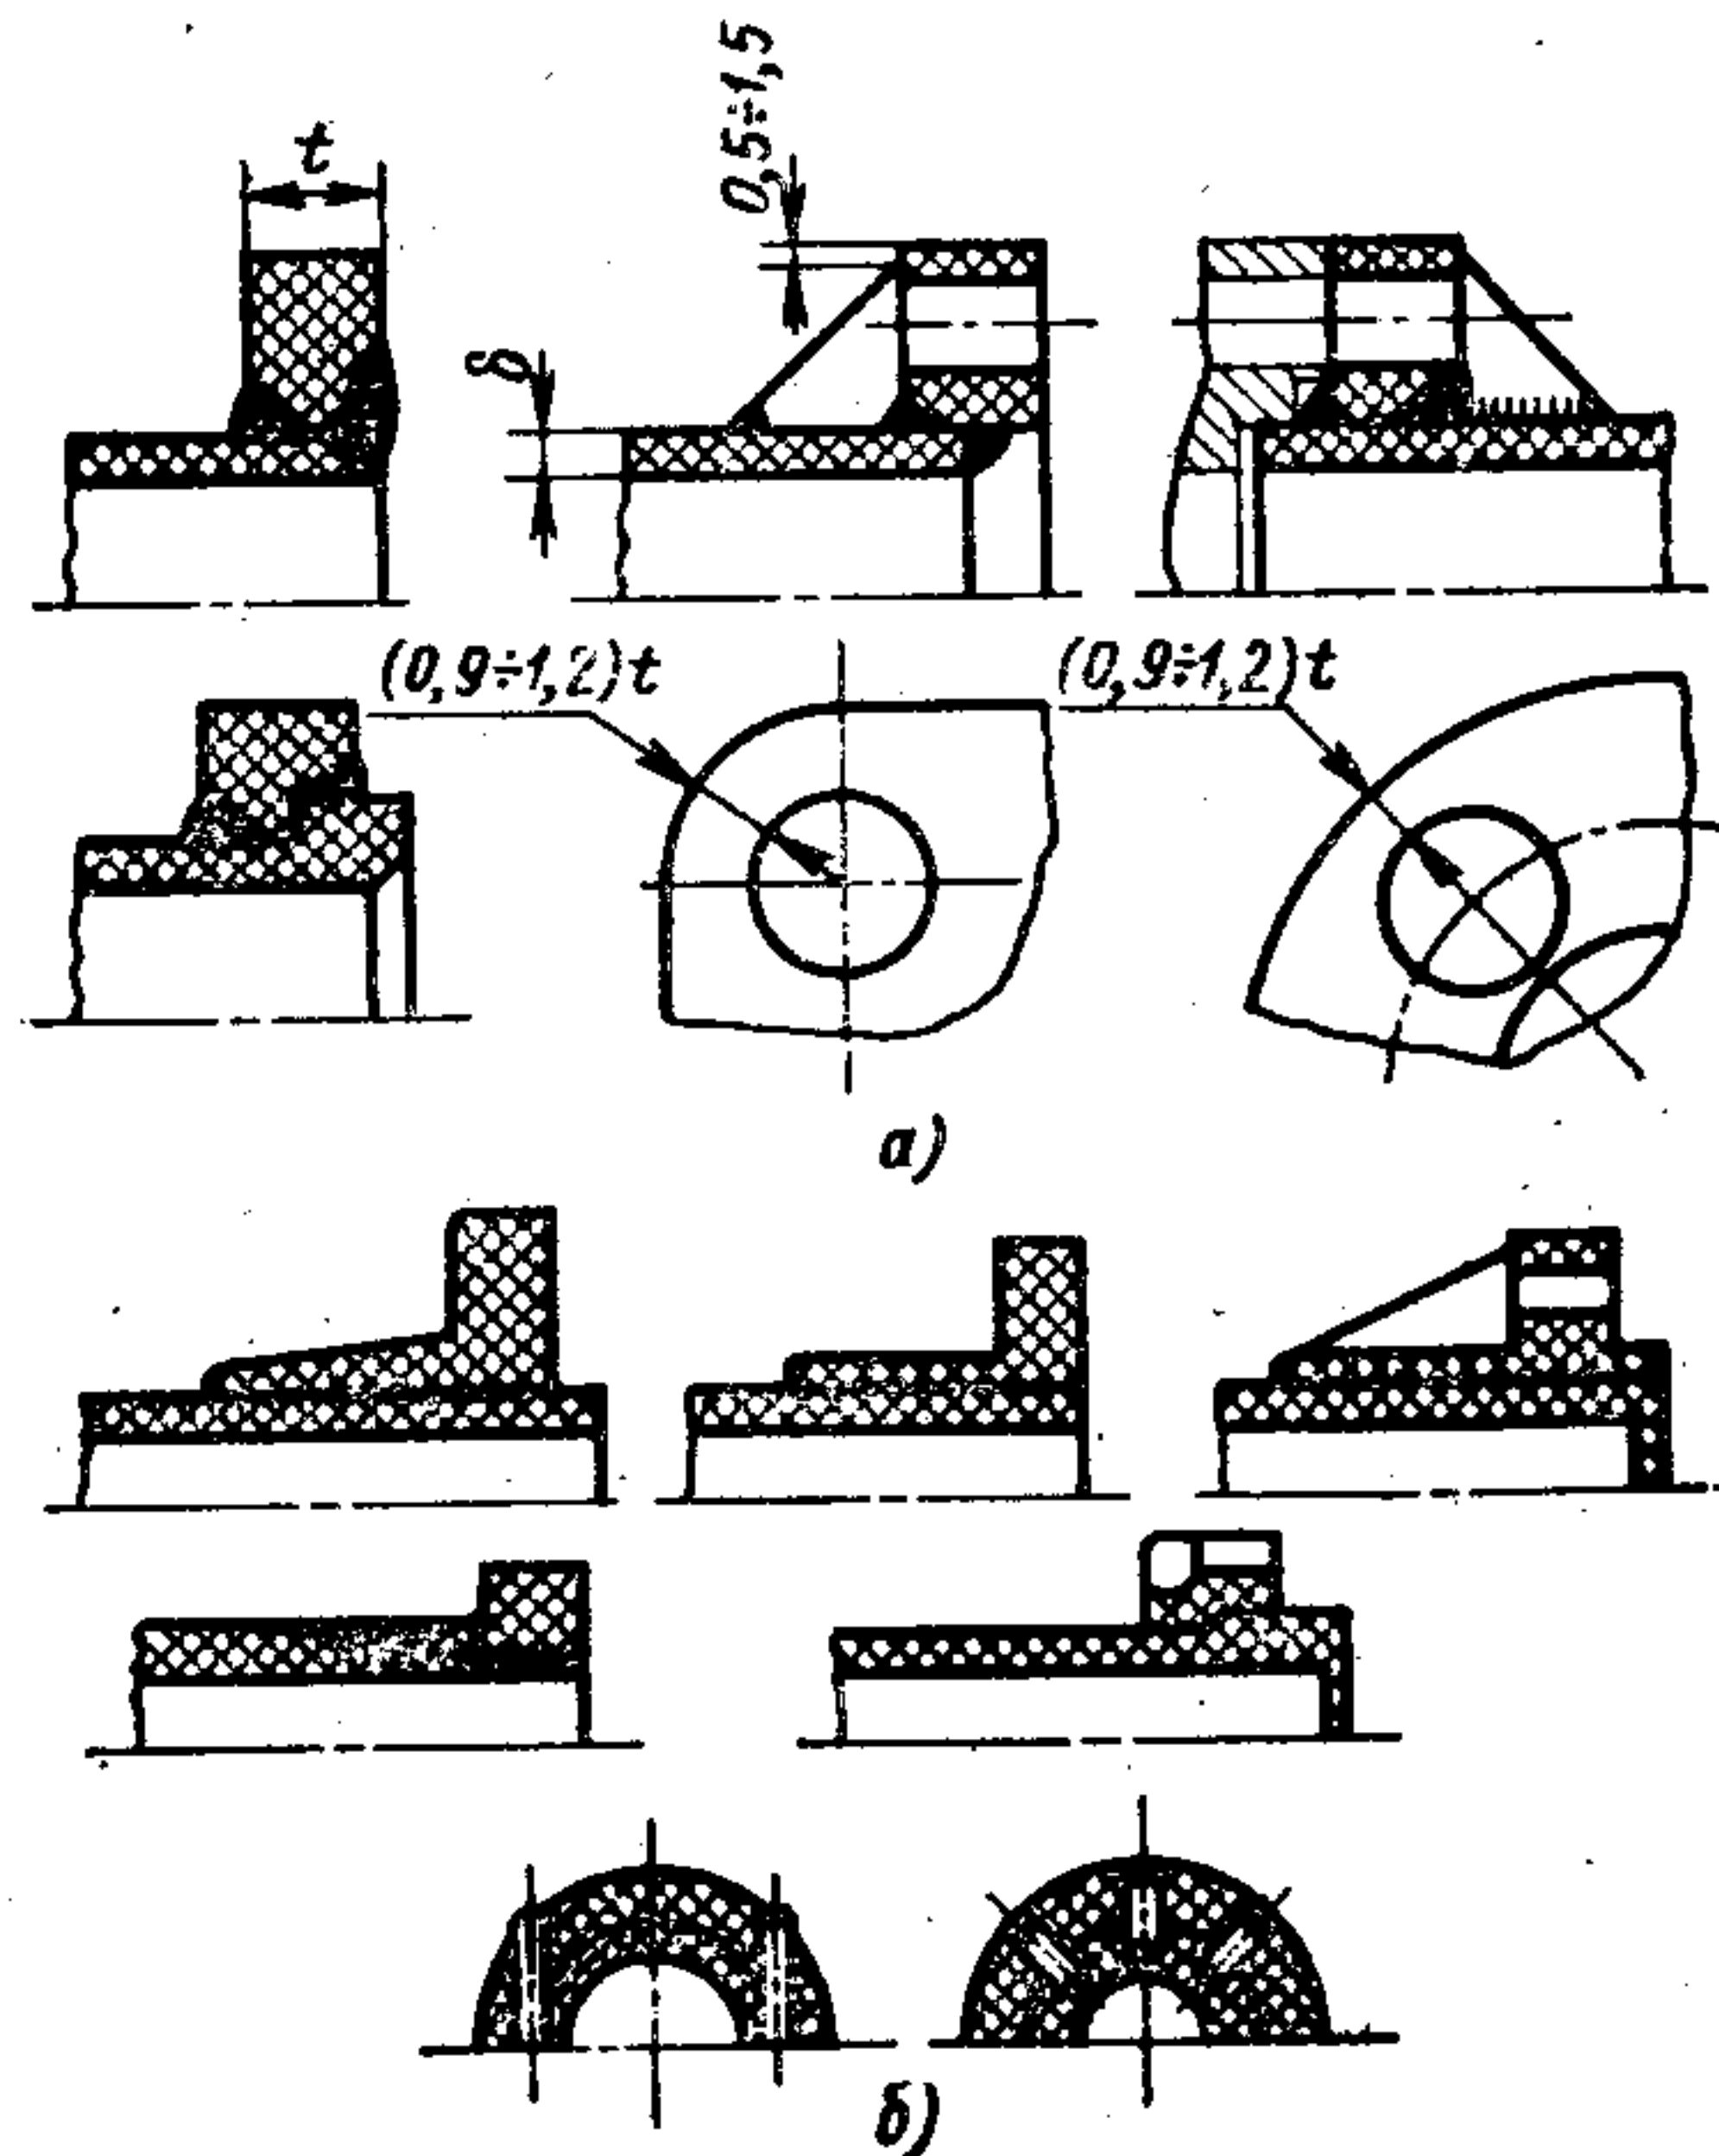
Конструкции сварных и клеевых соединений
